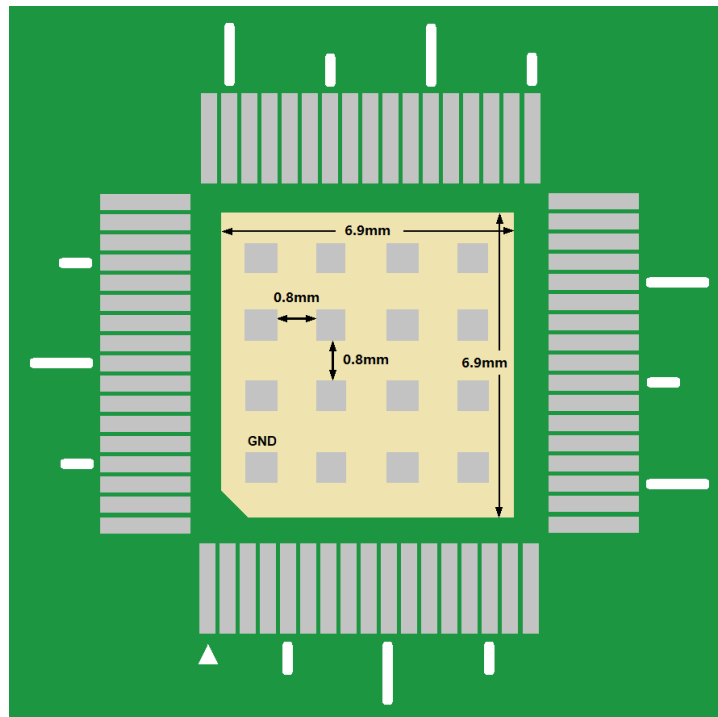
LT7580 底部焊盘 PCB 的设计建议
